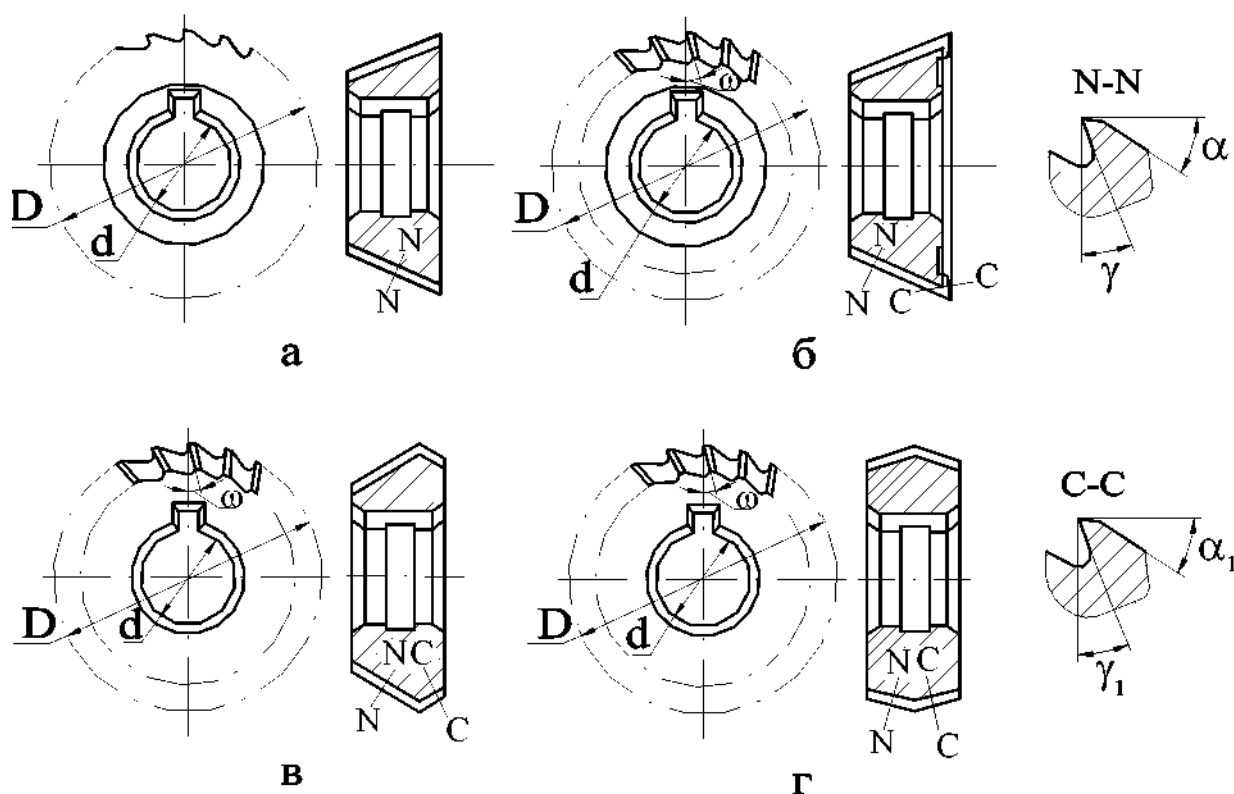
Конструктивные и геометрические параметры угловых фрез:
